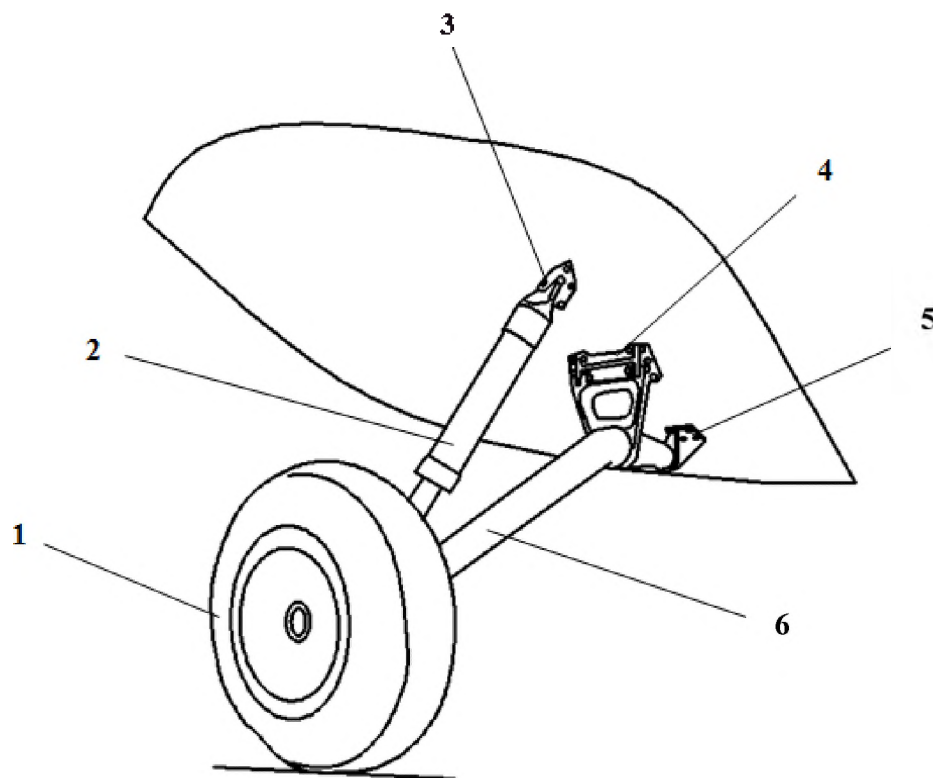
Конструкция основной стойки вертолета "АНСАТ-У":
